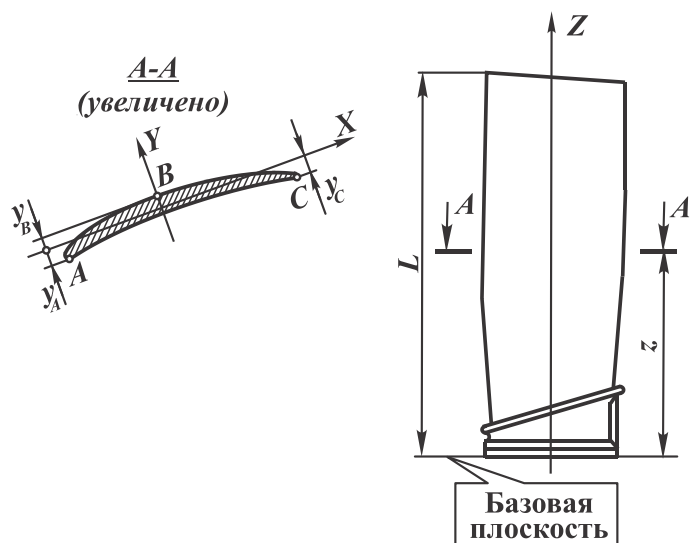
Лопатка 3-й ступени компрессора ГТД ТВ3-117
